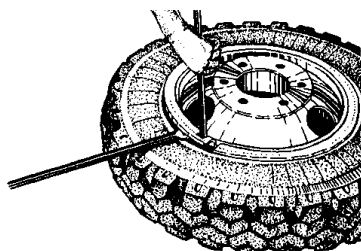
Установка прямой лопатки в прорезь бортового кольца
